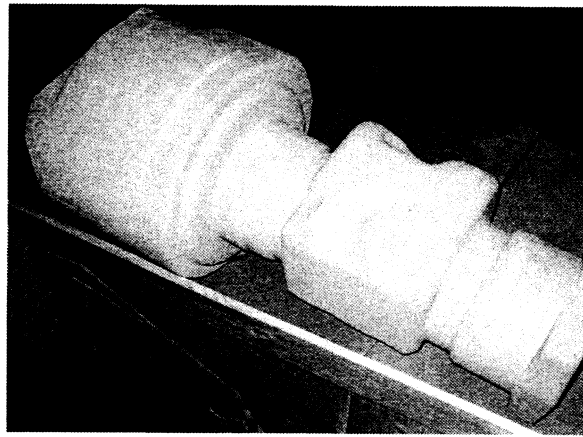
Сплошной стержень отливки «Рукав полуоси»
